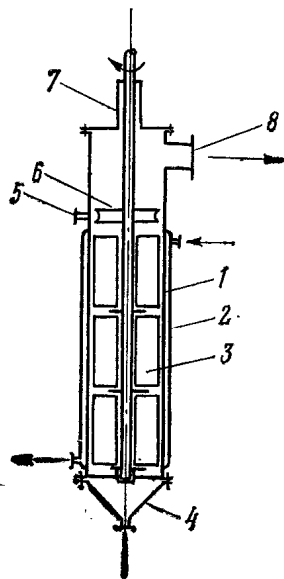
Пленочный испаритель с роторной мешалкой: 1 — корпус аппарата; 2 — паровая рубашка; 3 — роторная мешалка; 4 — конусное днище; 5 — штуцер для подачи раствора; 6 — распределительное кольцо для подачи раствора; 7 — приводной вал роторной мешалки; 8 — выход вторичного пара
